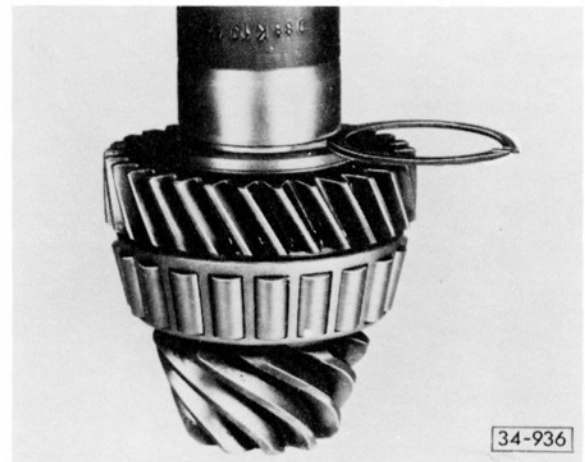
Axialspiel am Zahnrad für 4. Gang einstellen
